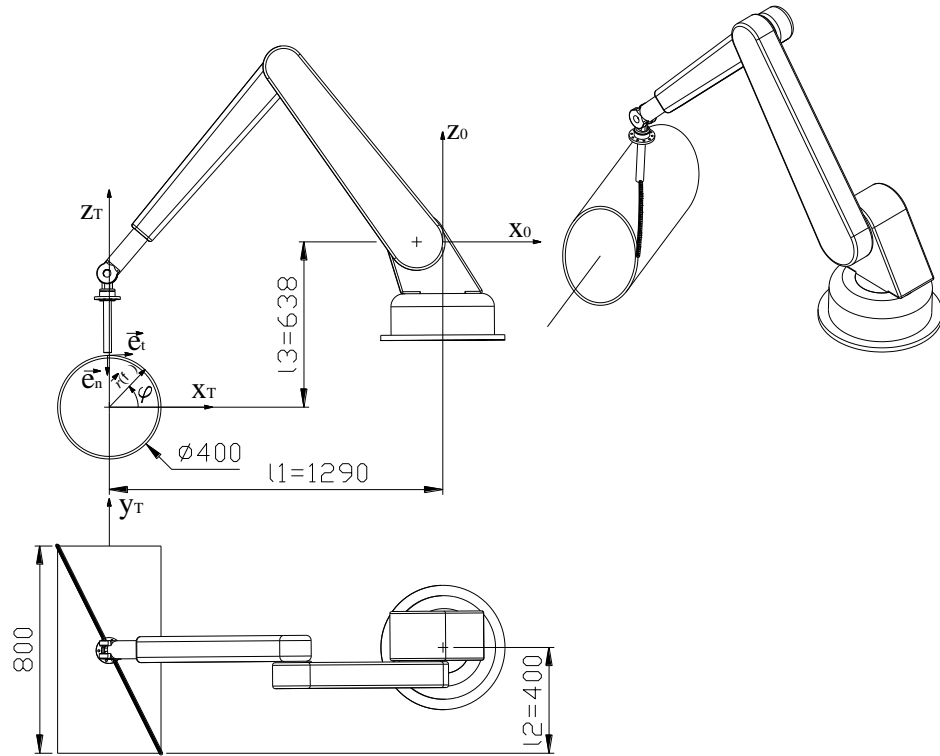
Exécution d'un joint de soudure de forme hélicoïdale par un robot manipulateur à 6 axes
